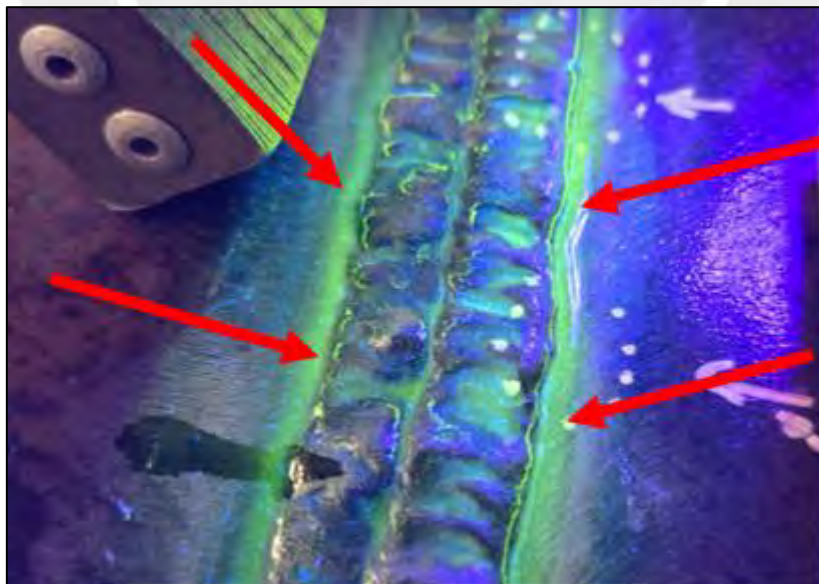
Indicaciones lineales sobre el cordón de soldadura
